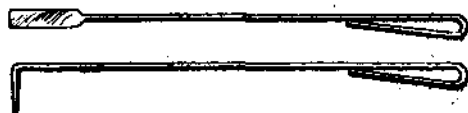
Вспомогательный инструмент для пудлинговой сварки алюминия (палочка).
